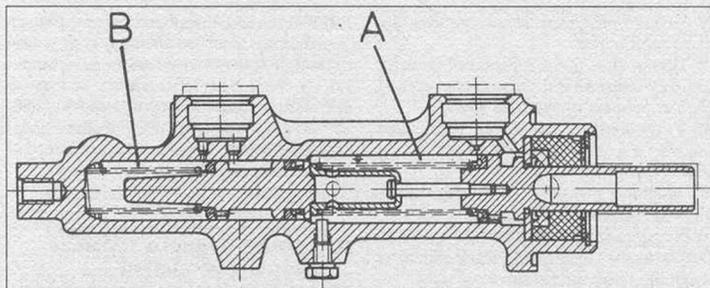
Профиль двойного главного тормозного цилиндра (Глава 11)
